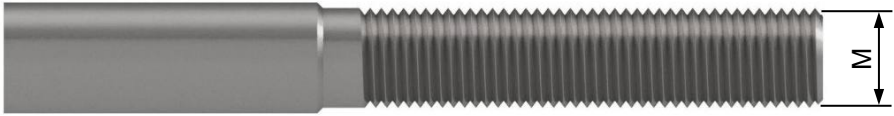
Gewindebolzen für Ankertypen G2, G3, G4 mit glattem Schaft
